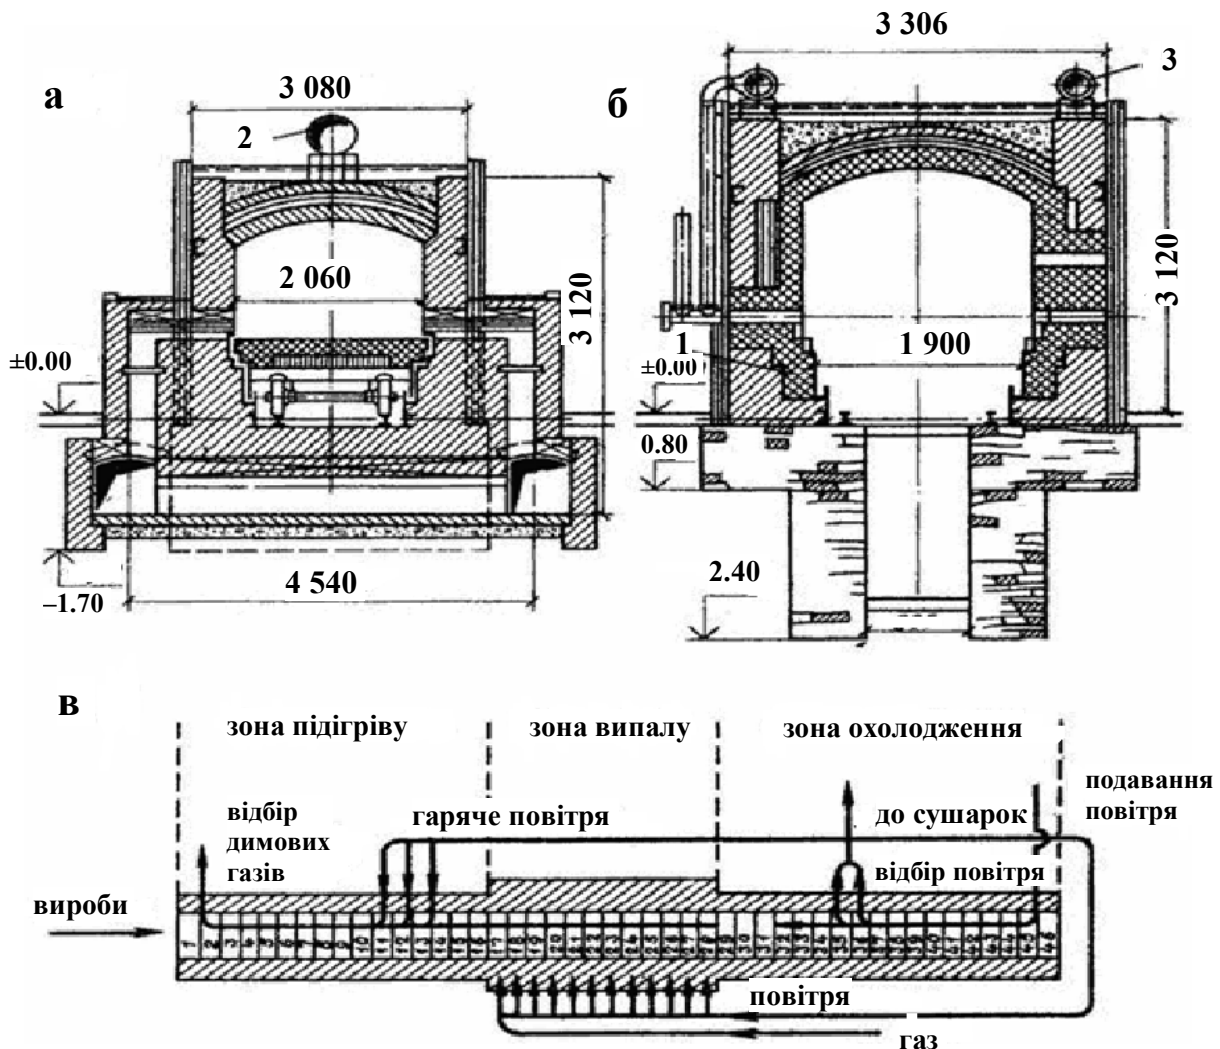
Тунельна піч: а – зона підігрівання; б – зона узвару; в – схема теплових зон; 1 – мурування; 2 – повітропровід; 3 – газопровід
